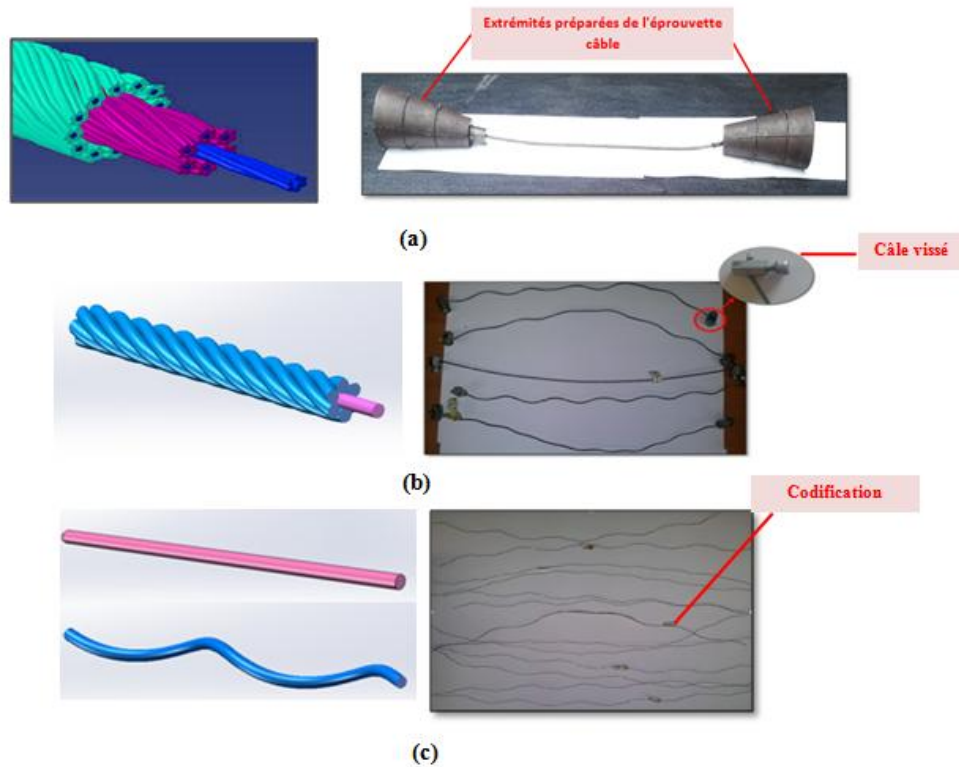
Dimensions des éprouvettes a) câble b) toron et c) fils
